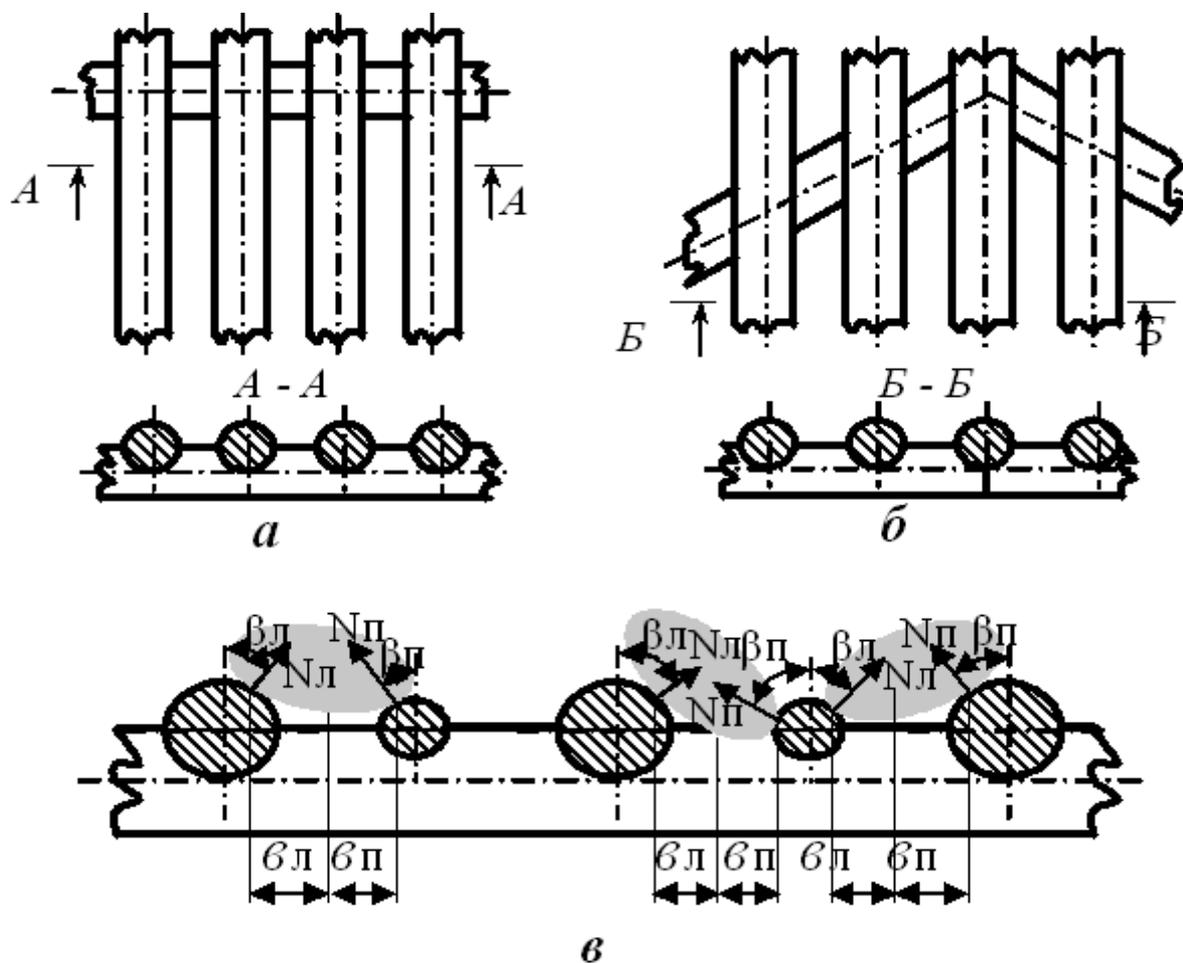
Предлагаемые решета проволоочно-сварной конструкции с круглыми перемычками
